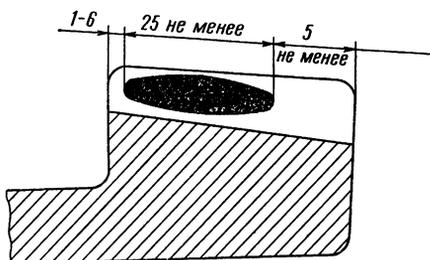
Расположение и размер пятна контакта в зацеплении для каждой из сторон зуба шестерен
